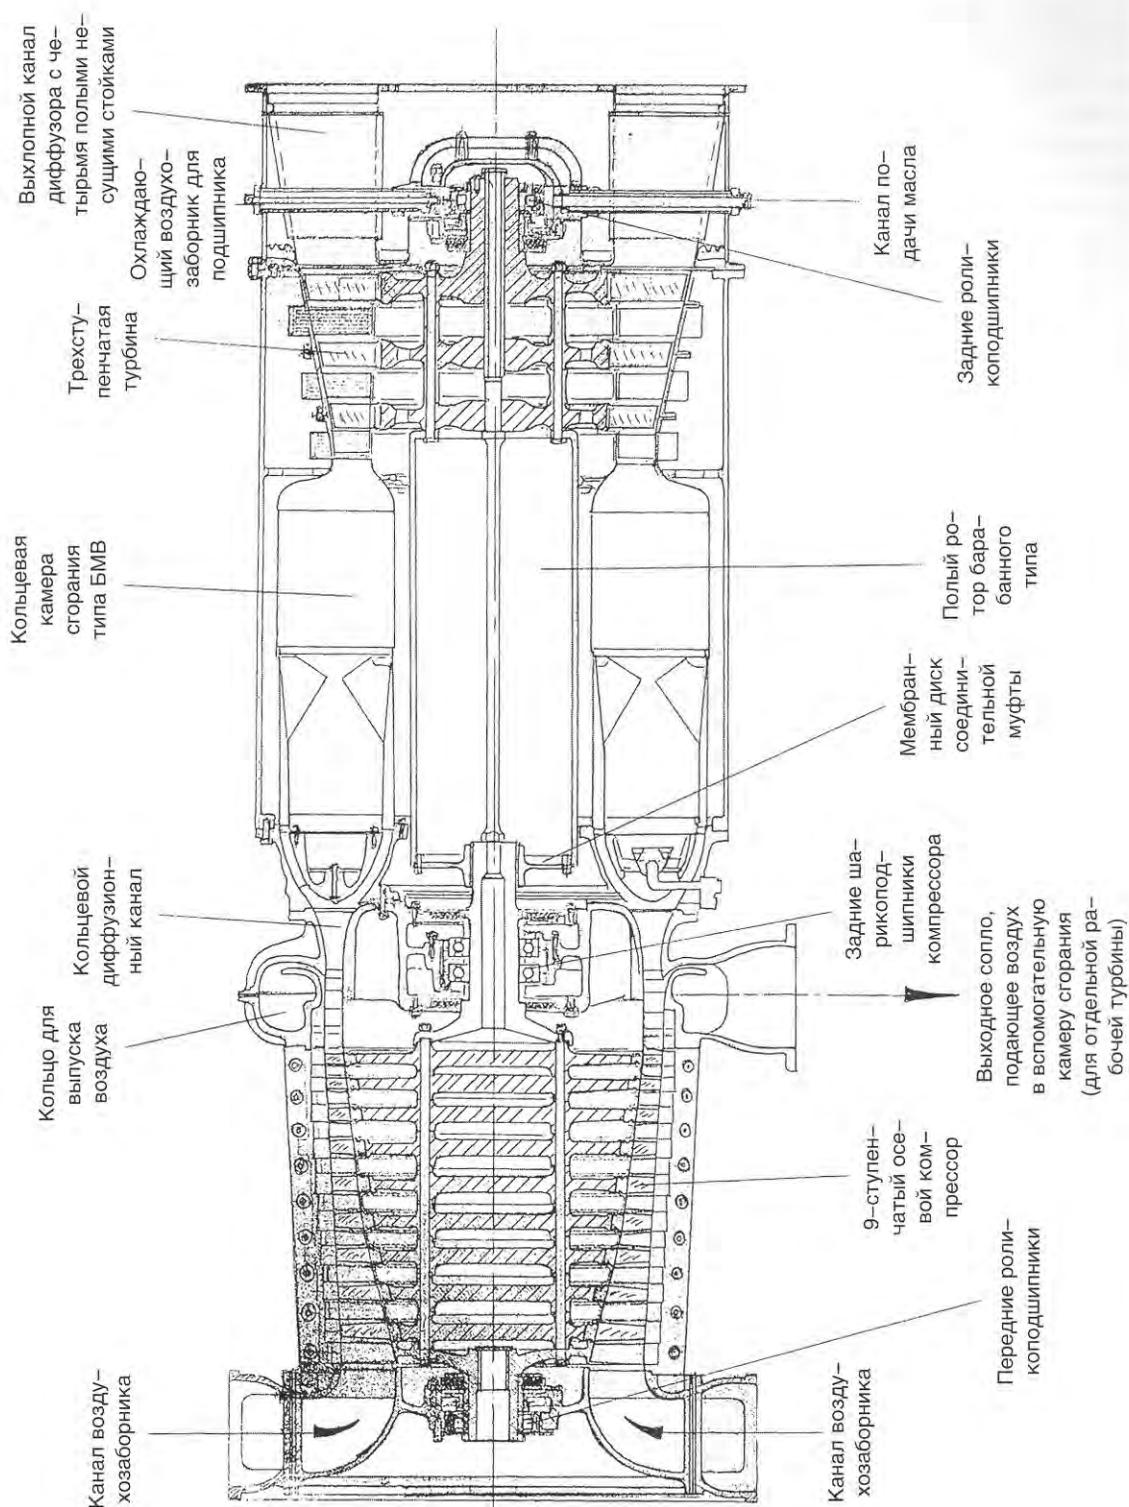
Компрессорной узел газовой турбины GT 102
